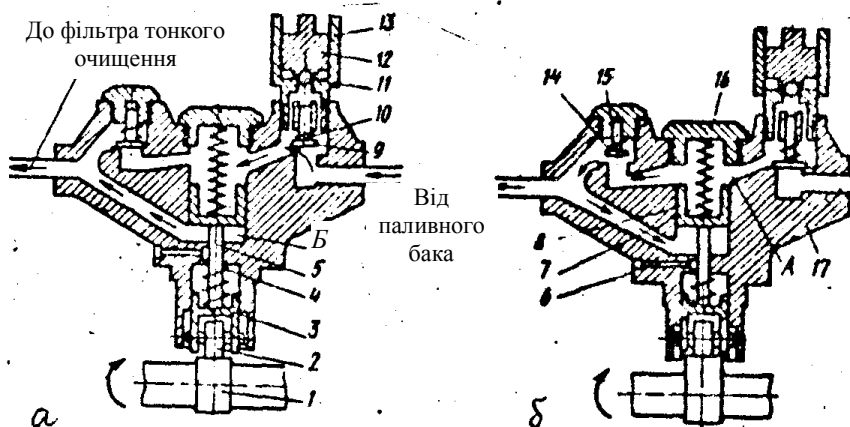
Схема роботи підкачувального насоса: 1 – ексцентрик; 2 – ролик штовхача; 3 – штовхач; 4 – пружина штовхача; 5 – шток поршня; 6 – канал; 7 – пружина поршня; 8 – поршень; 9 – впускний клапан; 10 – пружина впускного клапана; 11 – кульковий клапан; 12 – поршень ручного підкачувального насоса; 13 – циліндр ручного підкачувального насоса; 14 – пружина нагнітального клапана; 15 – нагнітальний клапан; 16 – пробка; 17 – корпус насоса; А – надпоршнева порожнина; Б – підпоршнева порожнина
